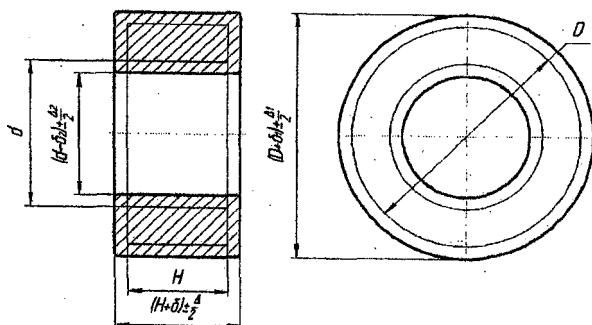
Схема назначения припусков и допусков для поковок 3-ей группы
